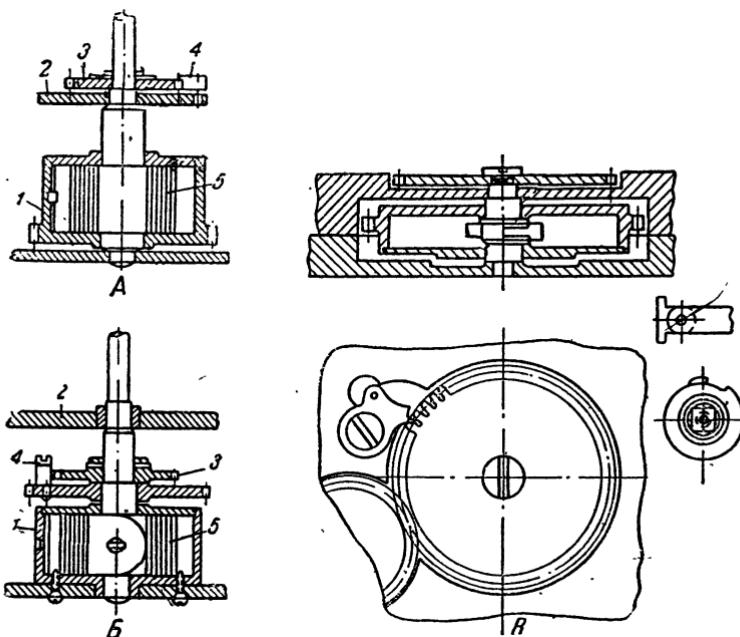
Типы барабанов: А—подвижный барабан; Б—неподвижный барабан; В—барабан карманных часов: 1—барабан; 2—передняя пластина; 3—храповое колесо; 4—храповая собачка; 5—пружина
